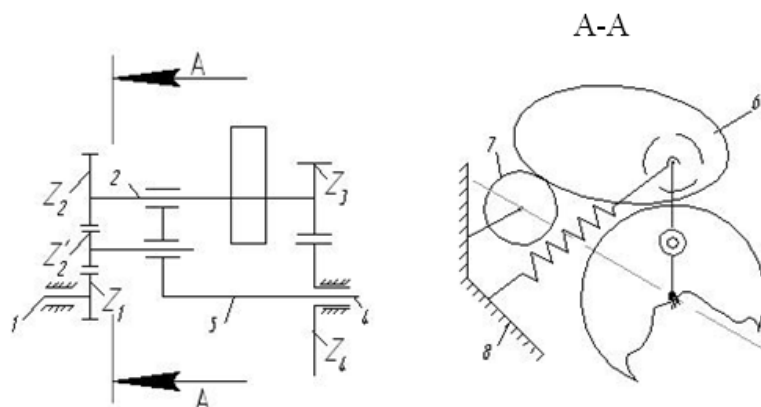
Кинематическая схема зубчато-рычажного механизма
